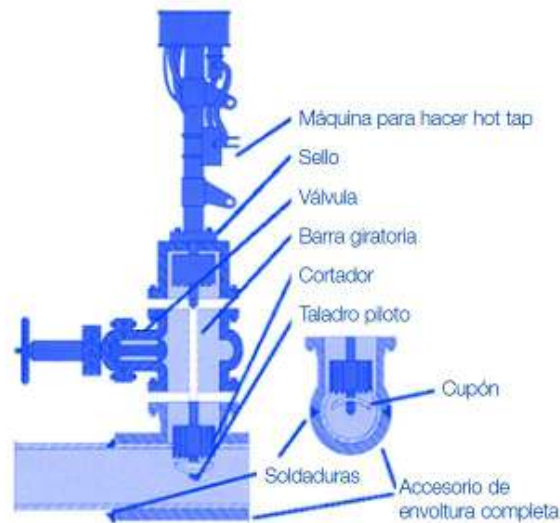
Partes Principales de la máquina de pegado (Hot Tap).
